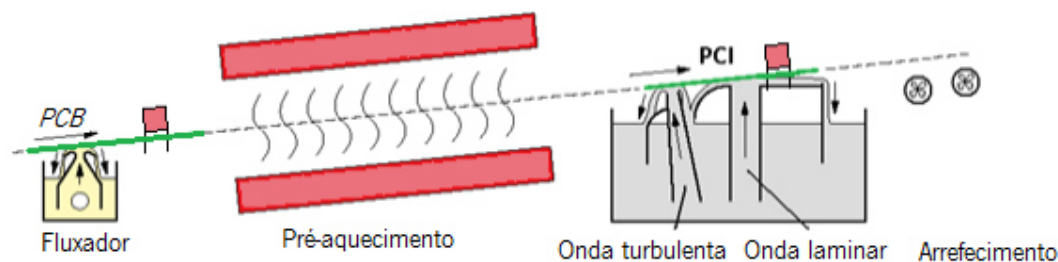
Soldadura por onda (adaptado de [21])
